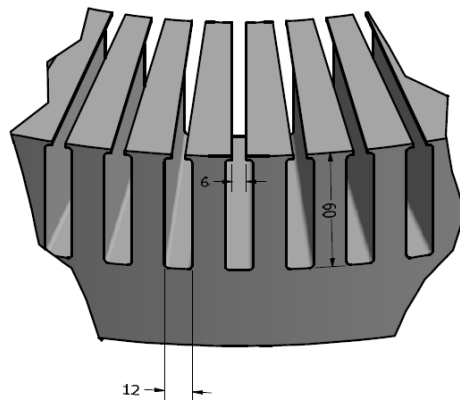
Dientes de estator de la máquina prototipo (dimensiones en [mm]).
